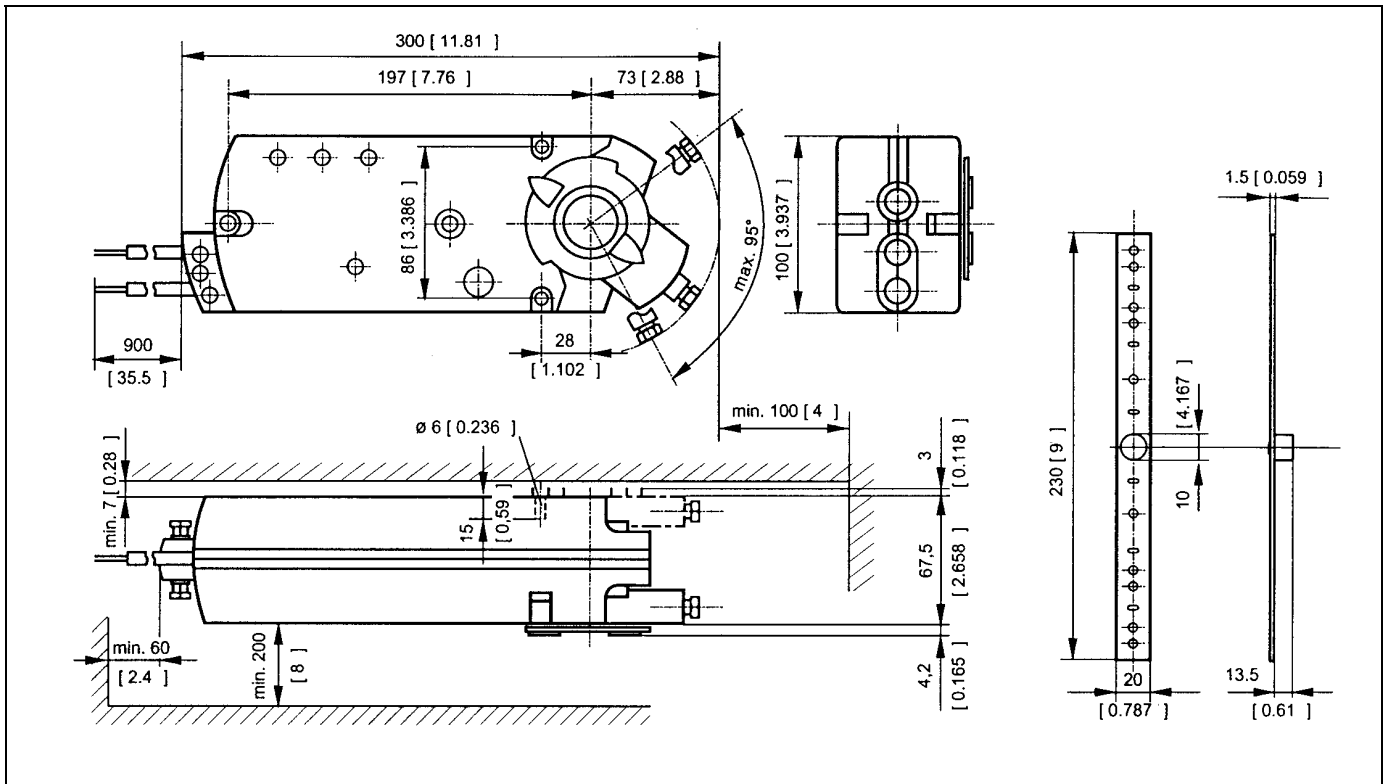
Dimensions ML4195E/8195E en mm [inch]
